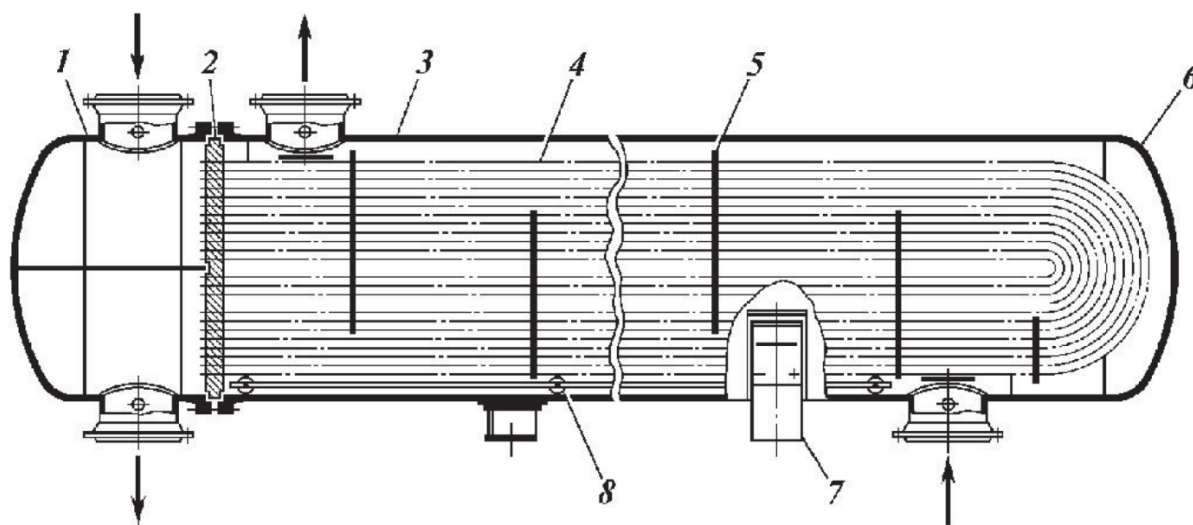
Кожухотрубчатый теплообменник с U-образными трубками
